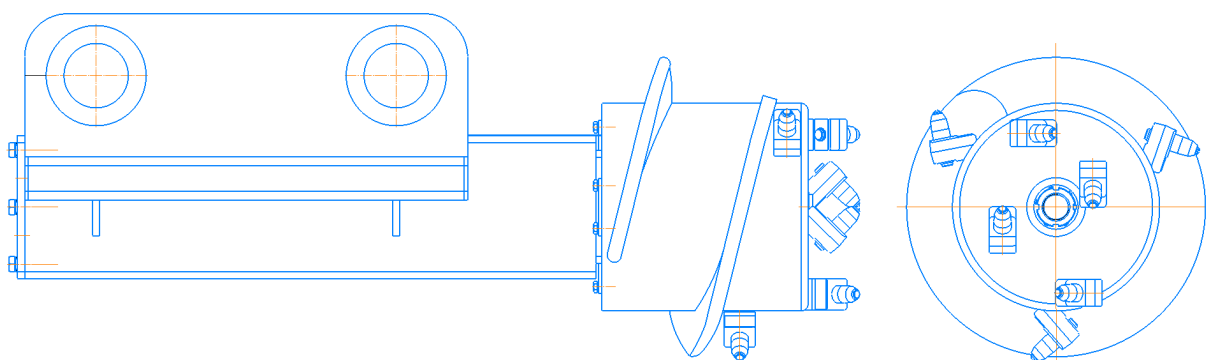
Общий вид фрезерного рабочего оборудования
